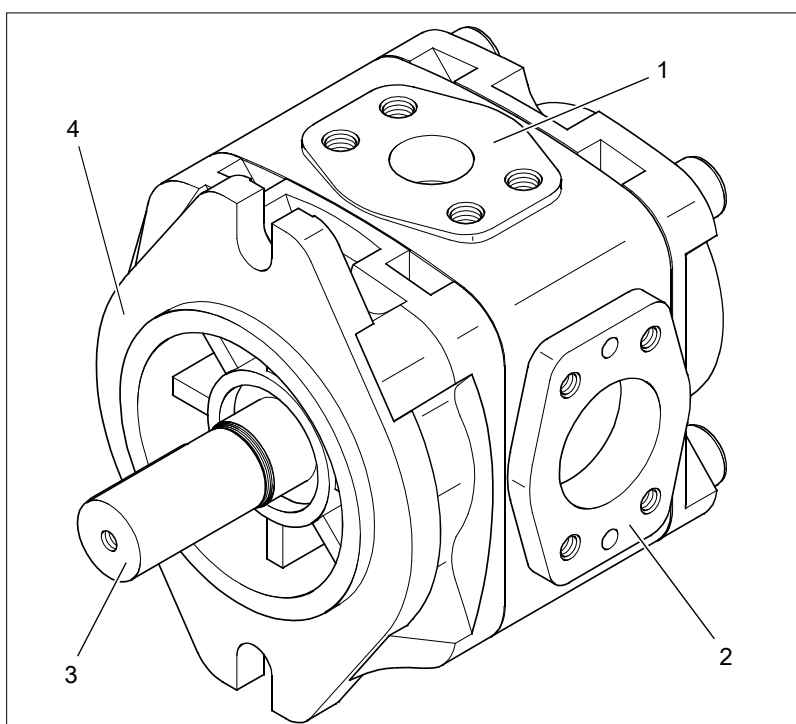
Montage Innenzahnradpumpe PGH.-3X
